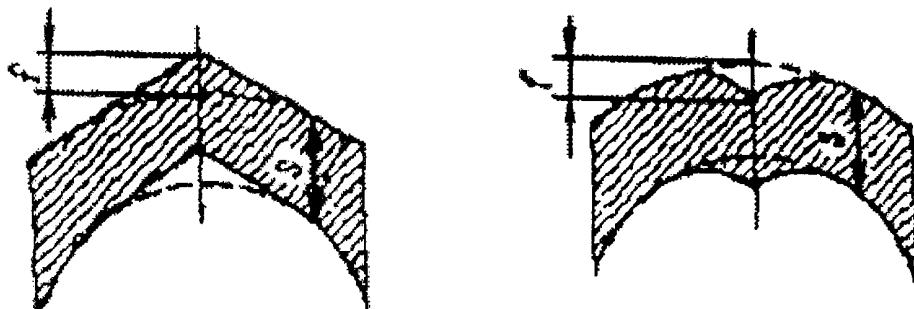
Увод (угловатость) кромок в сварных швах
